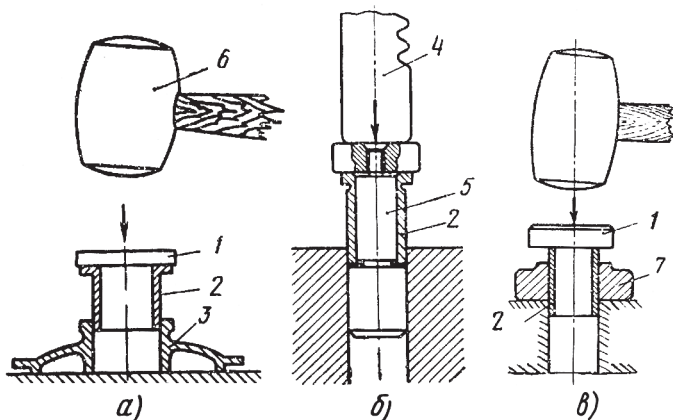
Запрессовка втулок в корпус подшипника:
